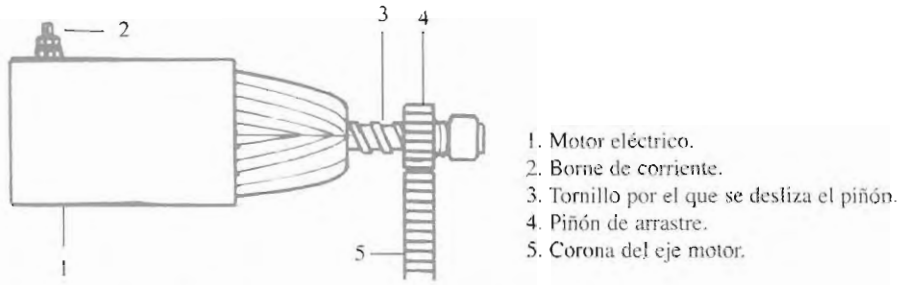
Motor eléctrico de arranque engranado al motor principal.
